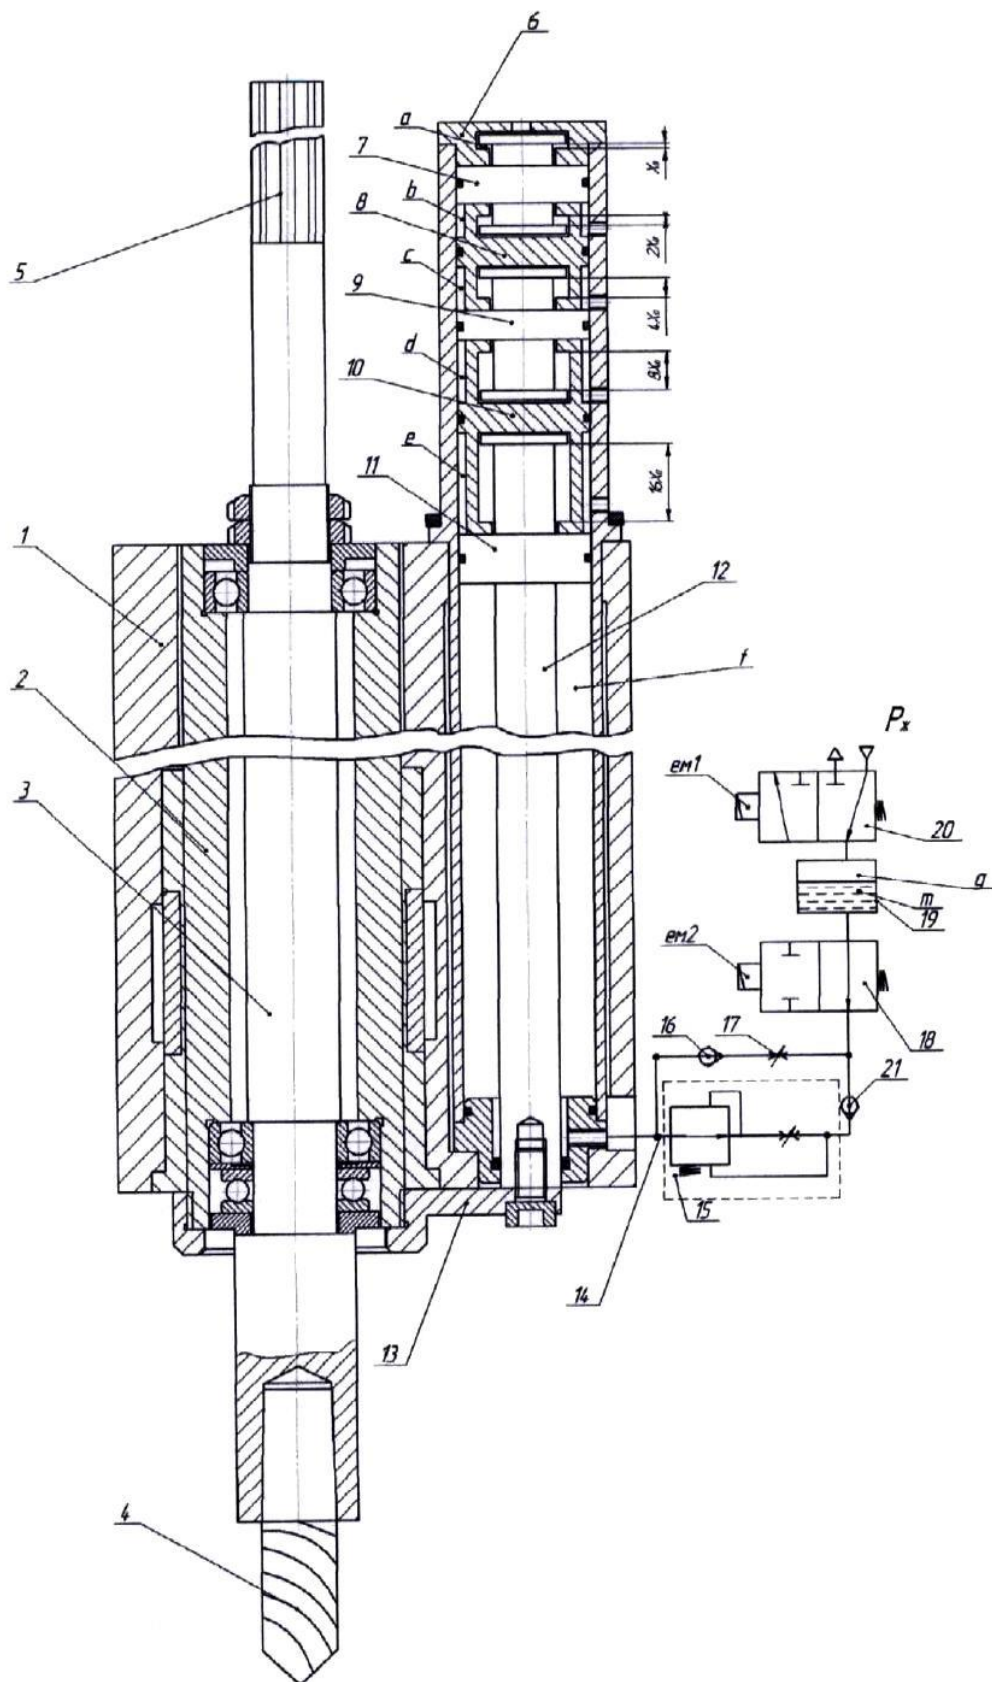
Механізм для подачі шпинделя свердлильного верстата
